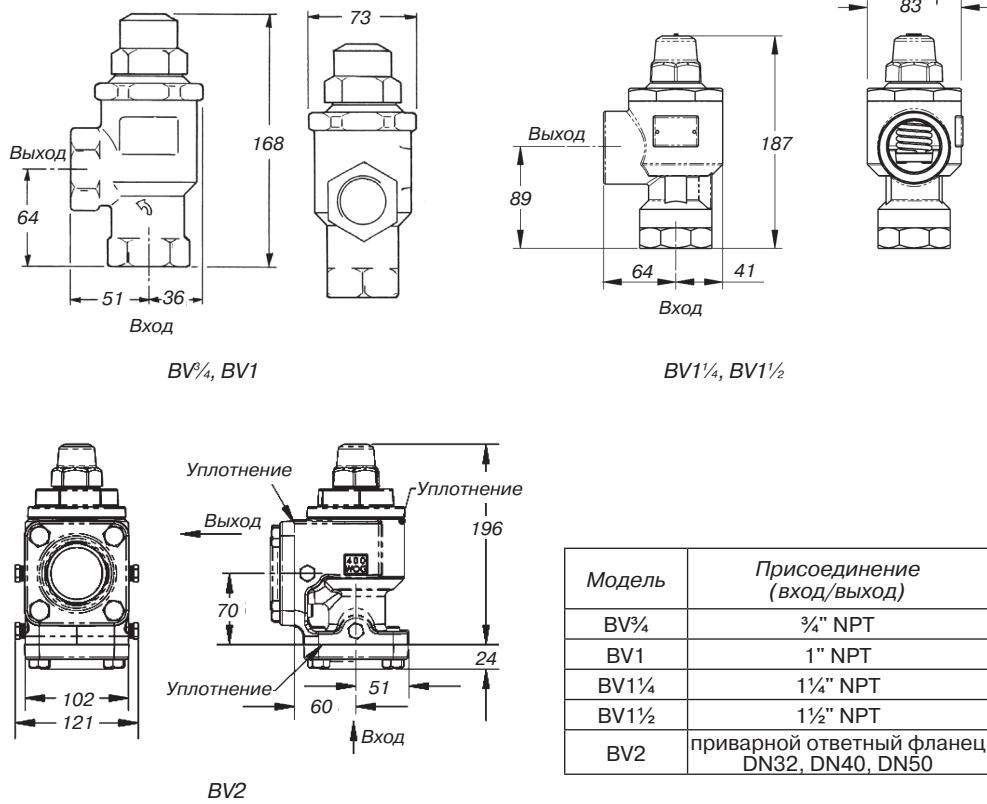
Габаритно-присоединительные размеры байпасных клапанов BV
